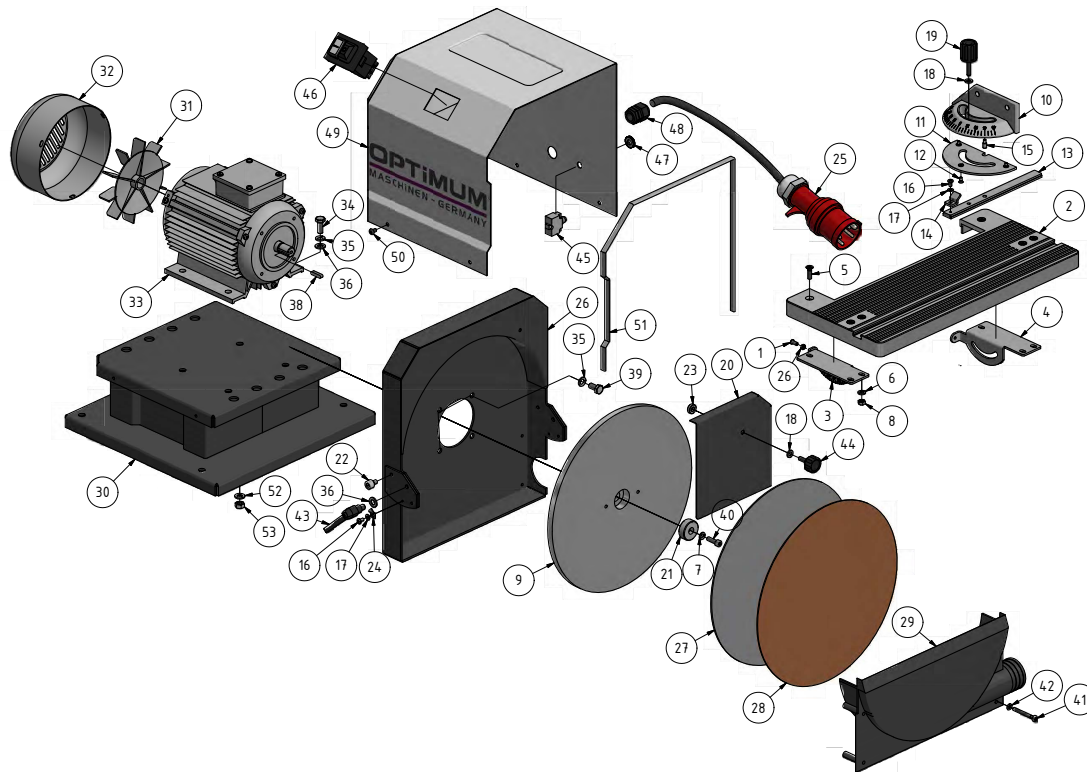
Ersatzteilzeichnung - Spare parts drawing
